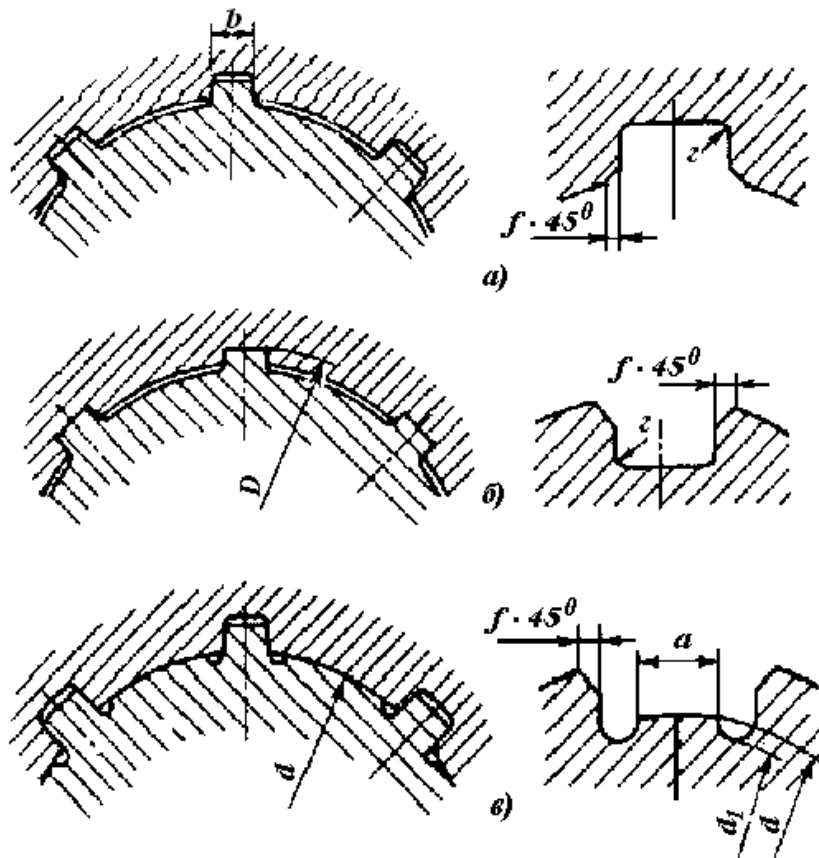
Схемы центрирования прямобоочных шлицевых соединений: *a* – по боковым поверхностям; *б* – по наружному диаметру; *в* – по внутреннему диаметру; схемы справа - форма сечения пазов ступицы (*a*) и вала (*б* и *в*)
